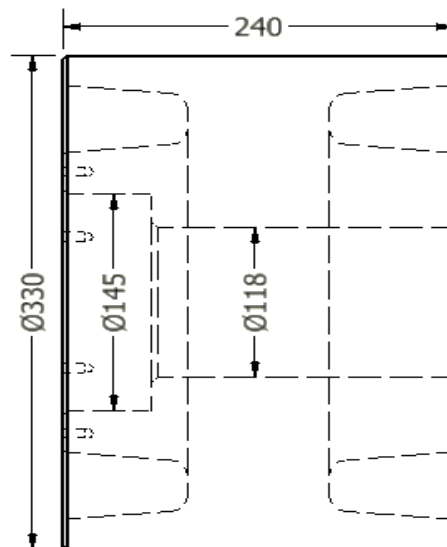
Geometria e dimensões da roda de decapagem [mm].
